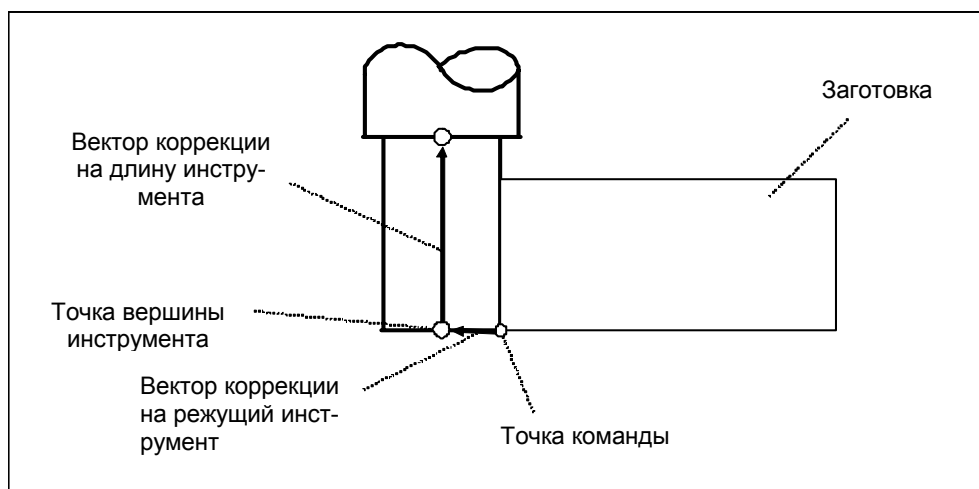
(л) Коррекция на режущий инструмент, когда отсутствует погрешность установки заготовки
